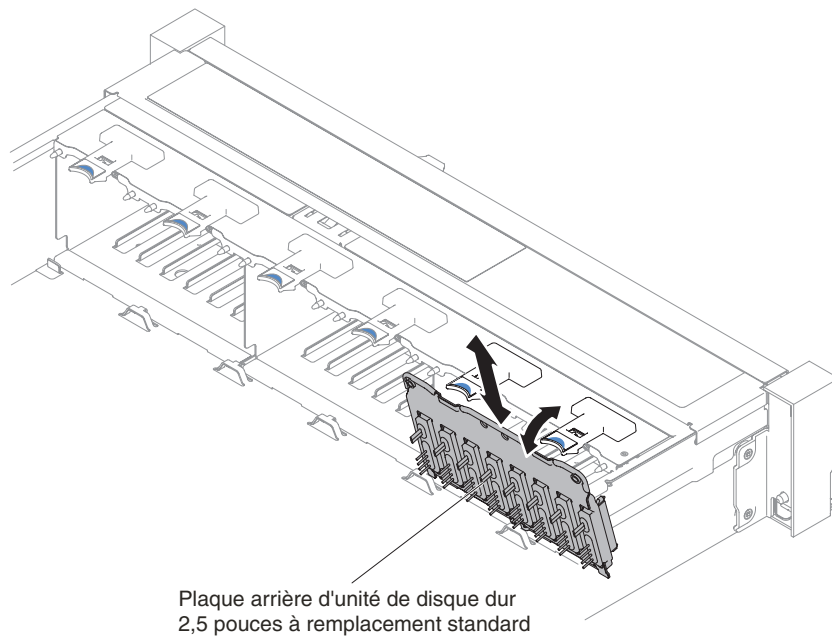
Installation de la plaque arrière d'unité de disque dur /du fond de panier remplaçable à chaud 2,5 pouces
